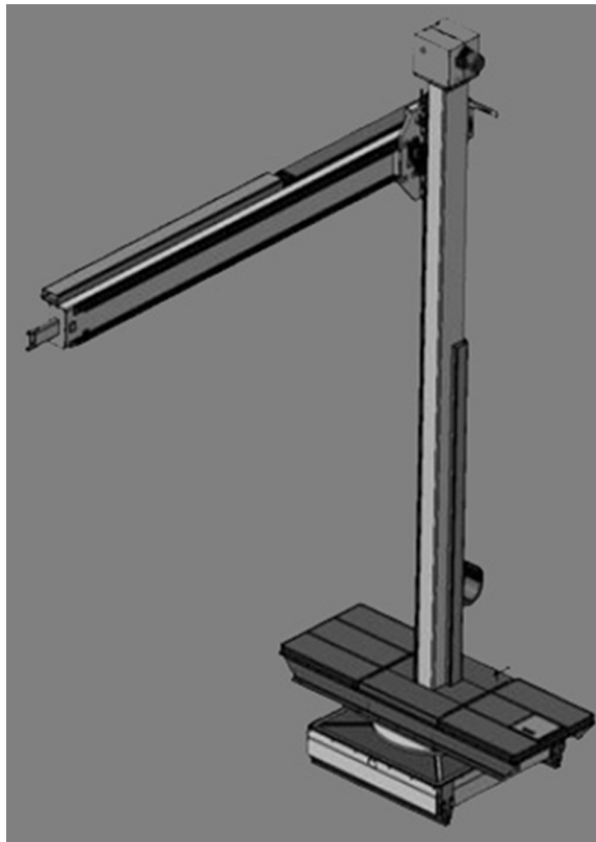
Coluna de Soldadura Simples [24]
